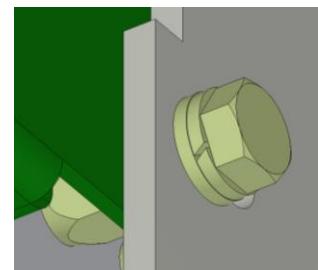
Установка крышки для ВЭ с ВМП-10К
